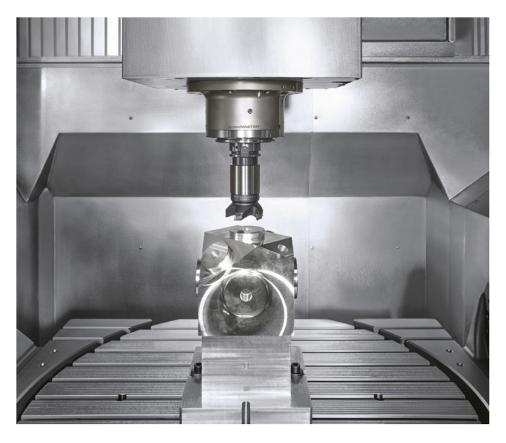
Für die Bearbeitung von Metall werden eine sehr steife Maschine und starke Motoren benötigt. Die Abbildung zeigt die Innenansicht einer DMU 95 monoblock von DMG Mori (© DMG Mori).
